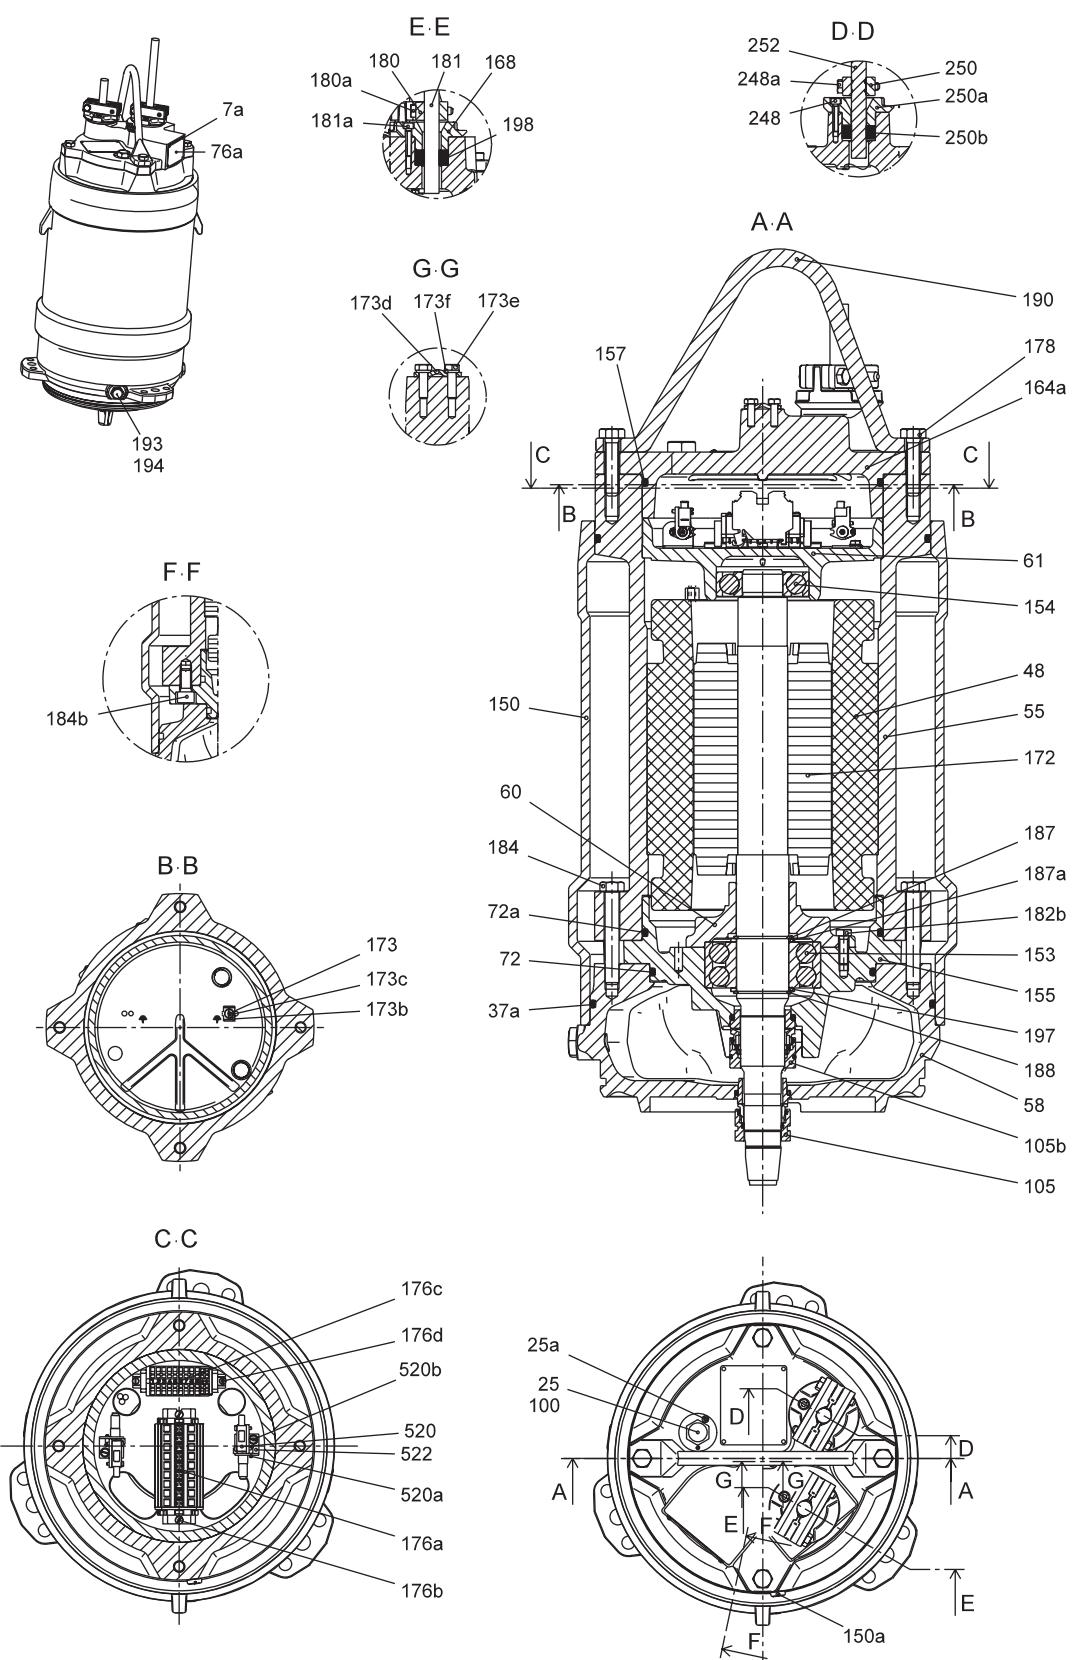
Взрывозащищённый двигатель без охлаждающего кожуха
